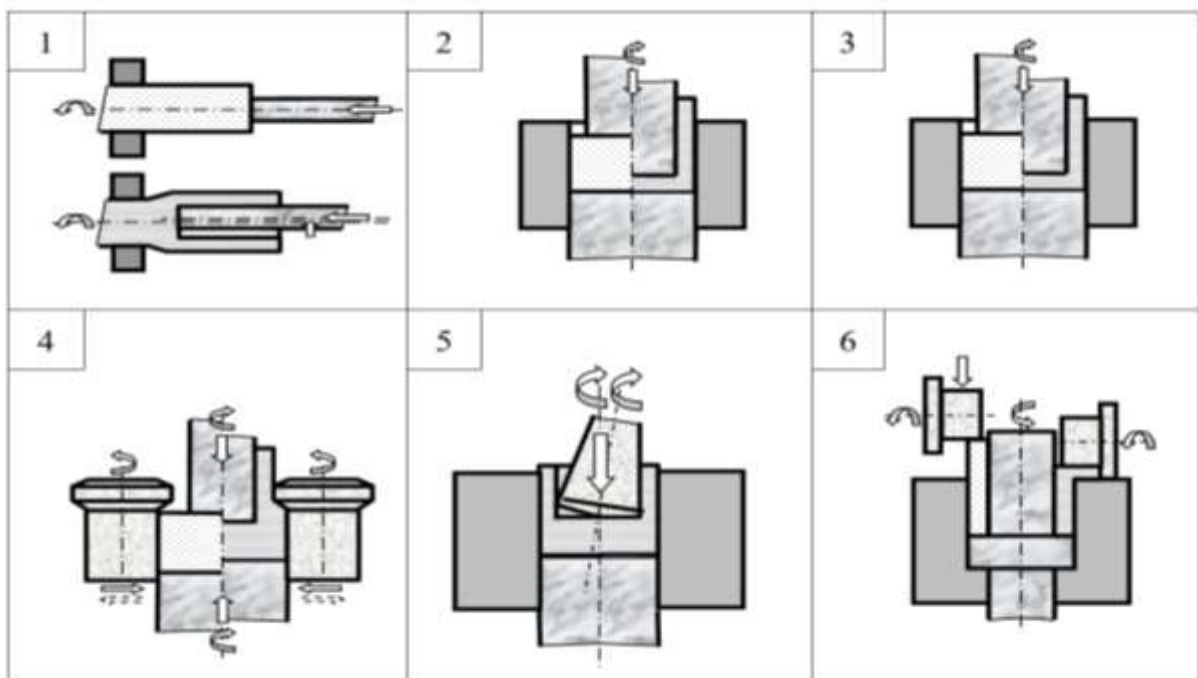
Способи виготовлення прецизійних деталей із різною кінематикою руху інструменту
